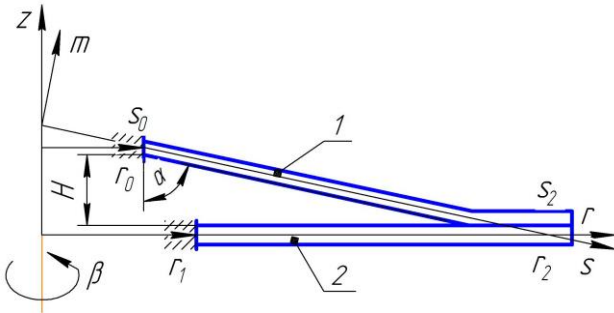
Розрахункова схема для визначення складальних напружень в деталях робочого колеса відцентрового вентилятора: 1 – конічна оболонка; 2 – кільцева пластинка.
